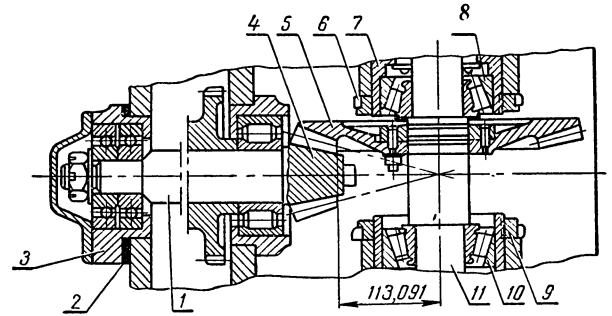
Схема регулировки главной передачи трактора Т-75:
